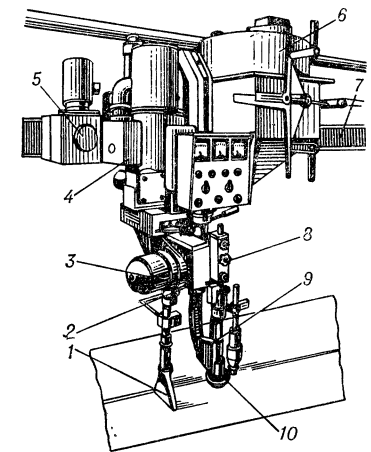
Сварочный автомат для дуговой сварки: 1 — флюсоотсос; 2 — сварочная головка; 3 — механизм подачи с редуктором; 4 — механизм подъёма; 5 — ходовой механизм; 6 — флюсоаппарат; 7 — рельсовый путь; 8 — подающий ролик; 9 — мундштук; 10 — воронка для флюса.
